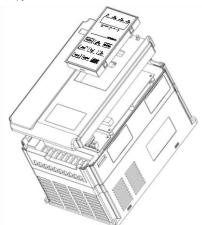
Схема демонтажа нижней крышки пластикового корпуса
